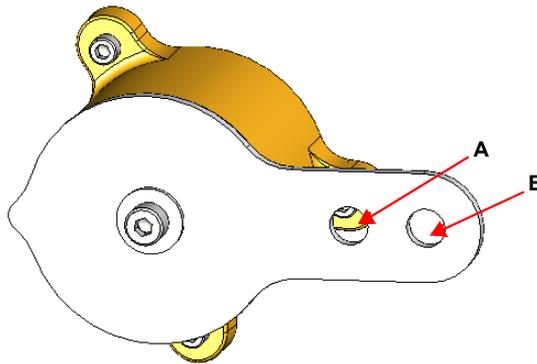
Palanca del SVi1000 instalada a un conjunto de IM
